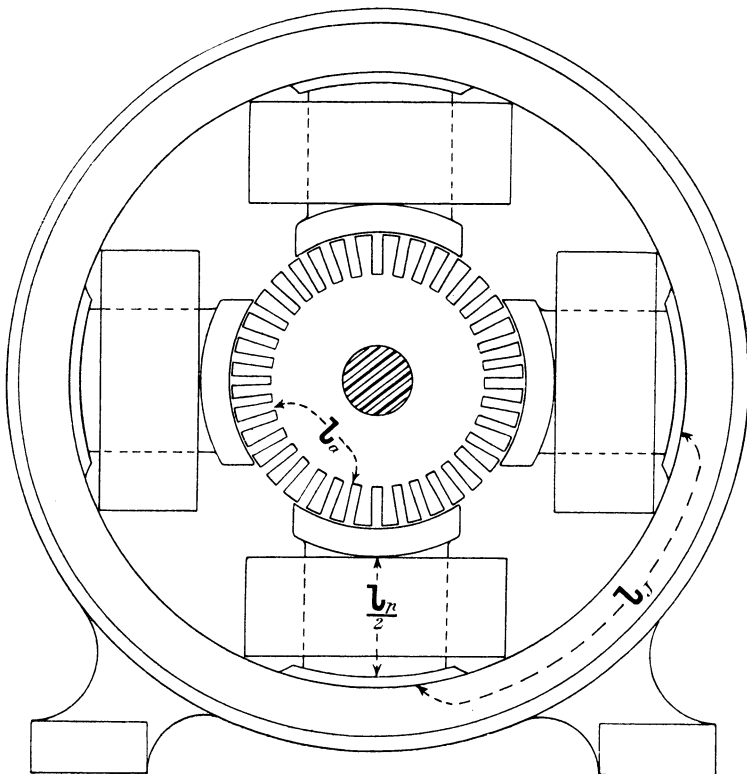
Schnittzeichnung einer vierpoligen Maschine.
